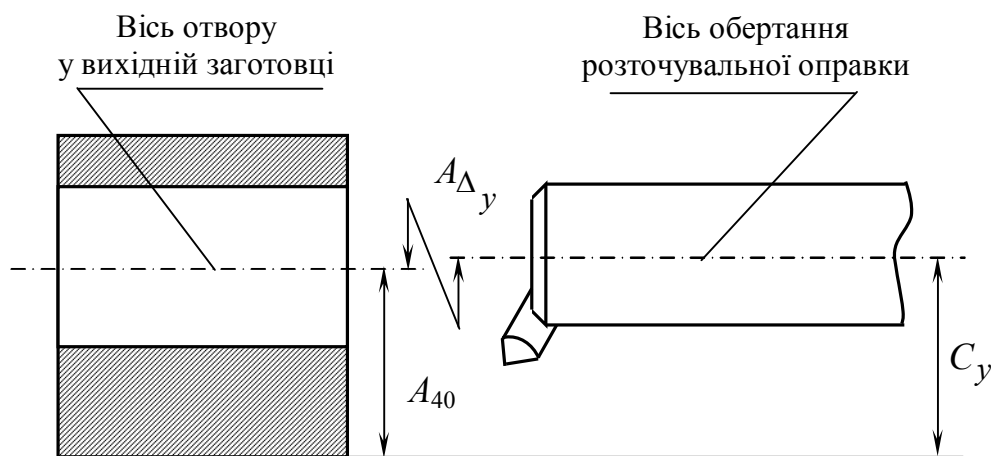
Схема розмірного ланцюга для визначення похибки базування у напрямі осі Y
